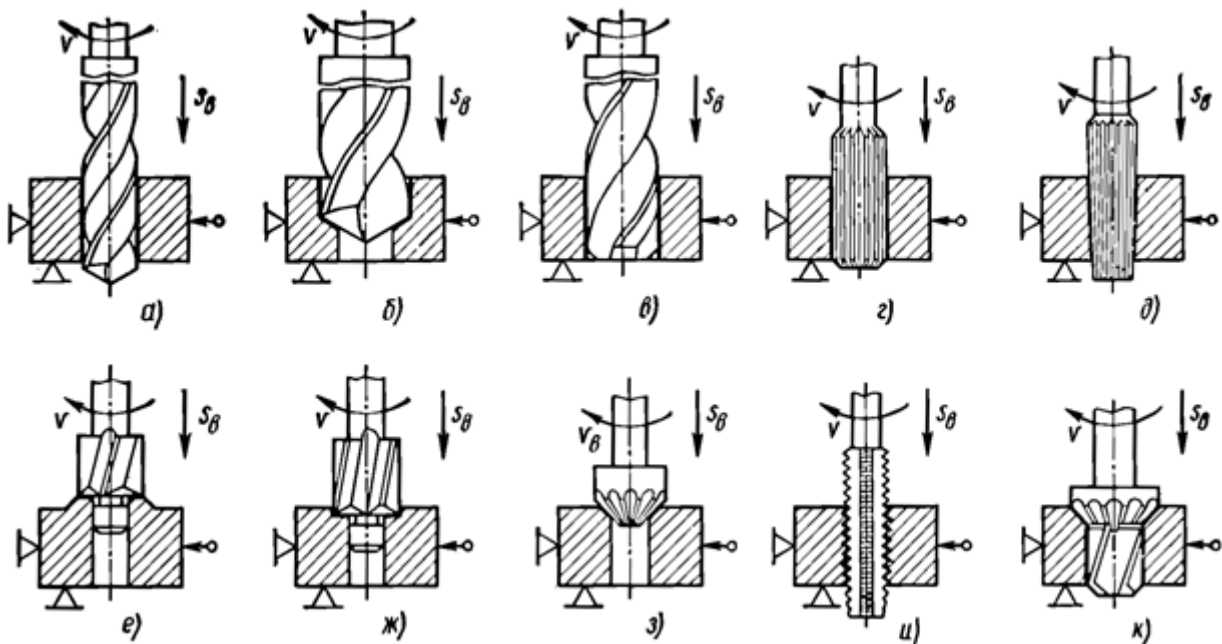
Схеми обробки заготовок на свердильних верстатах
